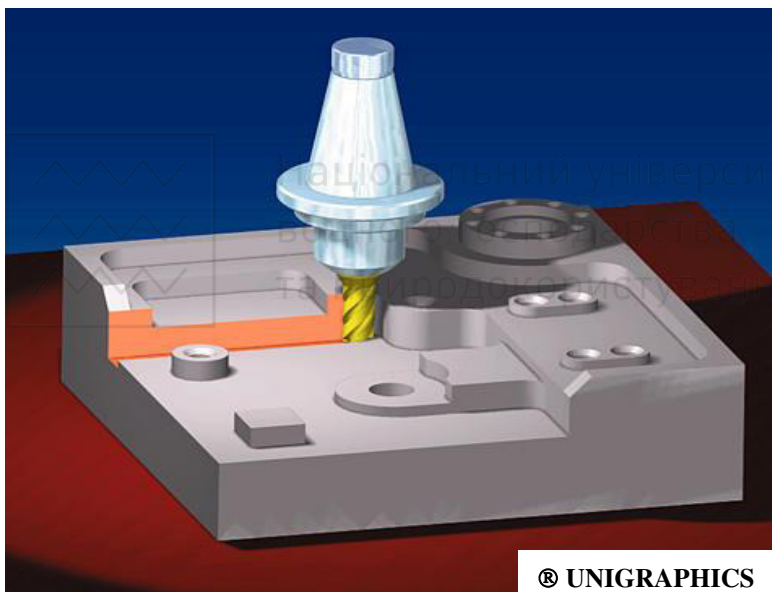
Моделювання процесів обробки деталей 2-2.5 ос. фрезеруванням в модулі UG/Planar Milling
